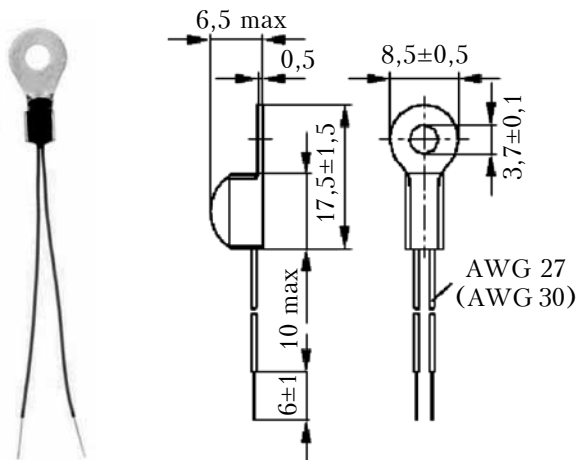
Внешний вид и габаритные размеры NTC-термистора B57703M0103G017
